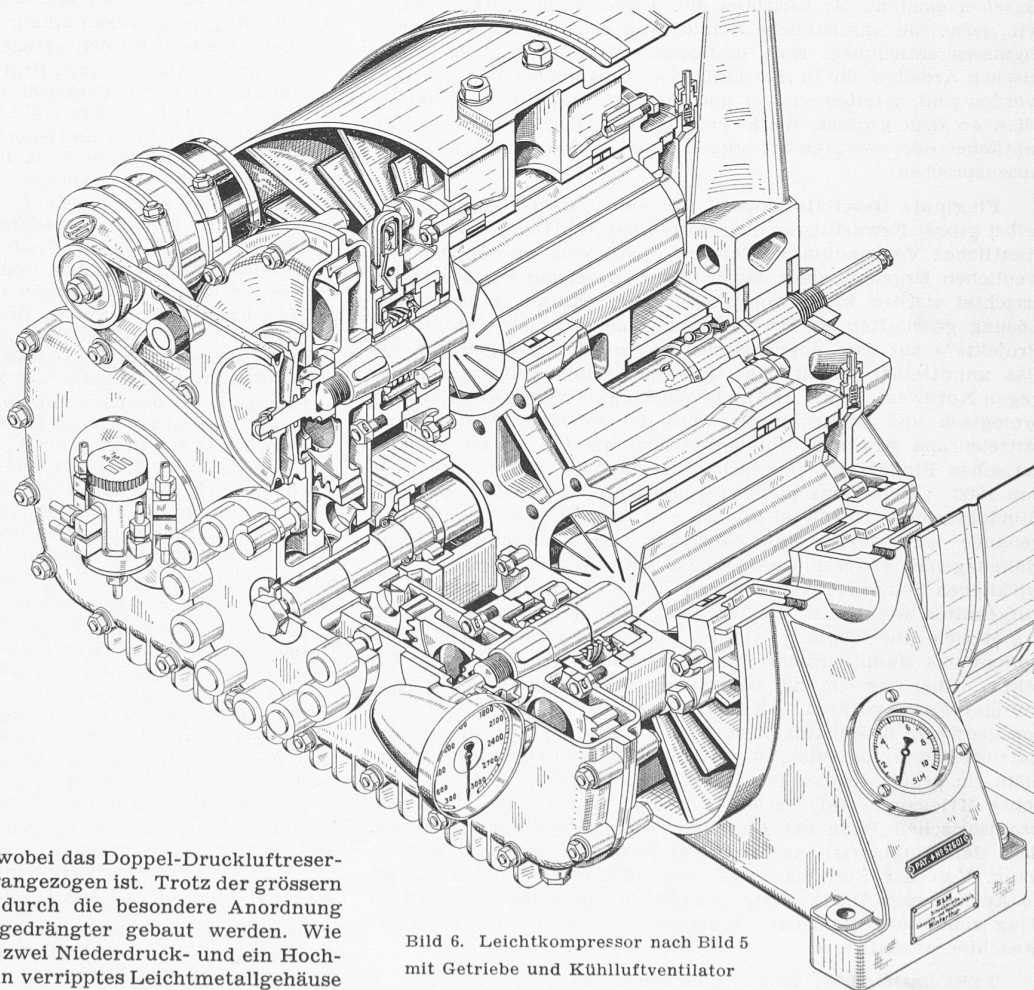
Leichtkompressor nach Bild 5 mit Getriebe und Kühlluftventilator
